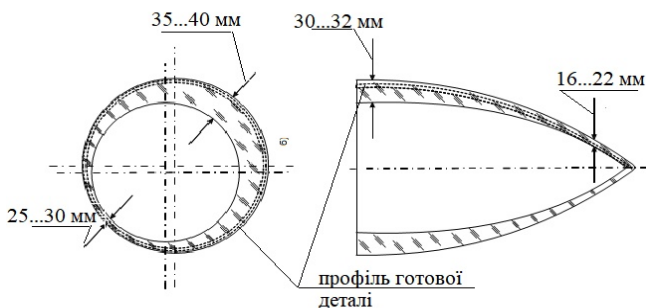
Схема відхилення профілю заготовки від профілю готового виробу
